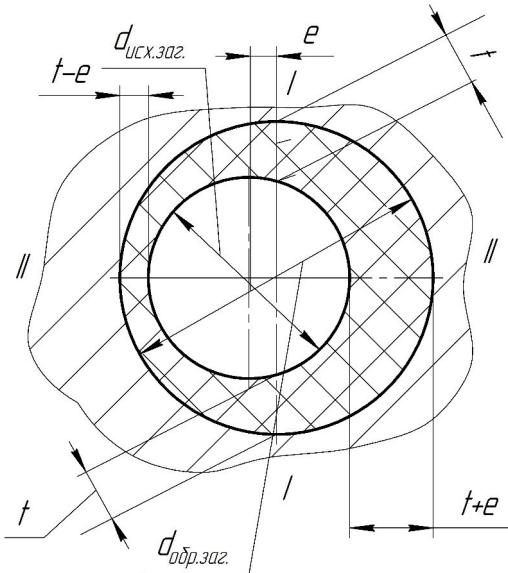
Схема образования неравномерного припуска от смещения оси заготовки:  $e$  – эксцентриситет;  $t$  – заданная глубина резания.
